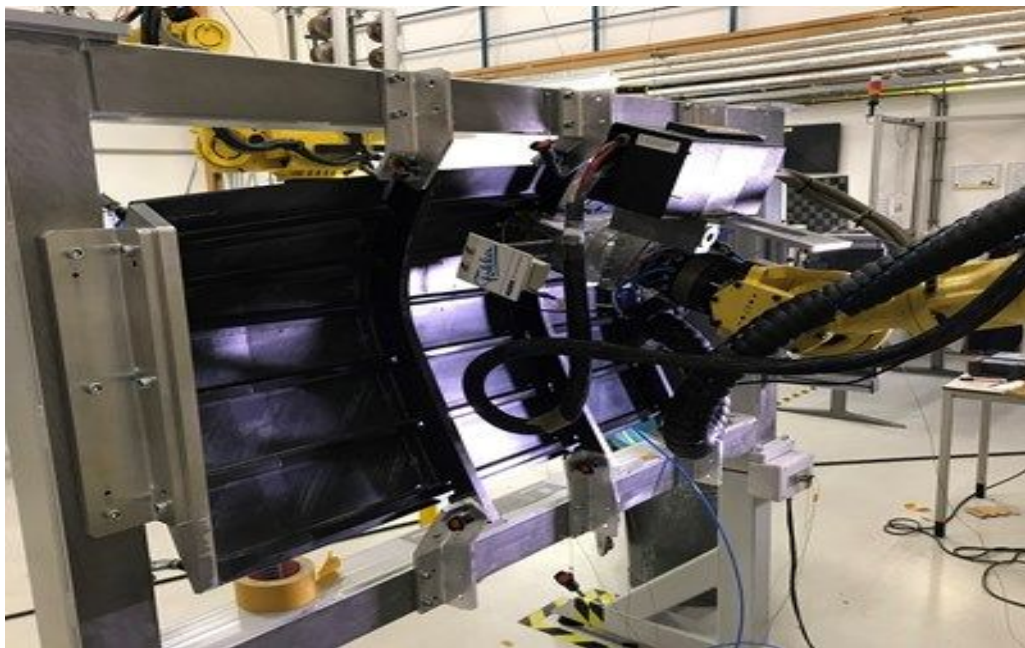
Автоматичне зварювання для з'єднання деталей з термопластів
